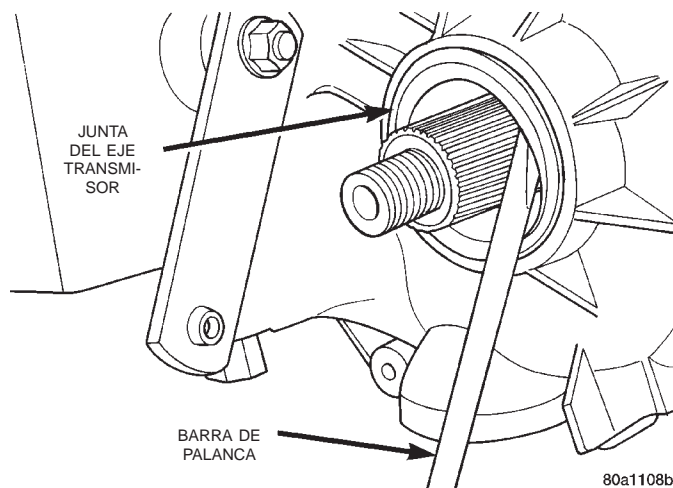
Desmontaje de la junta del eje transmisor delantero
